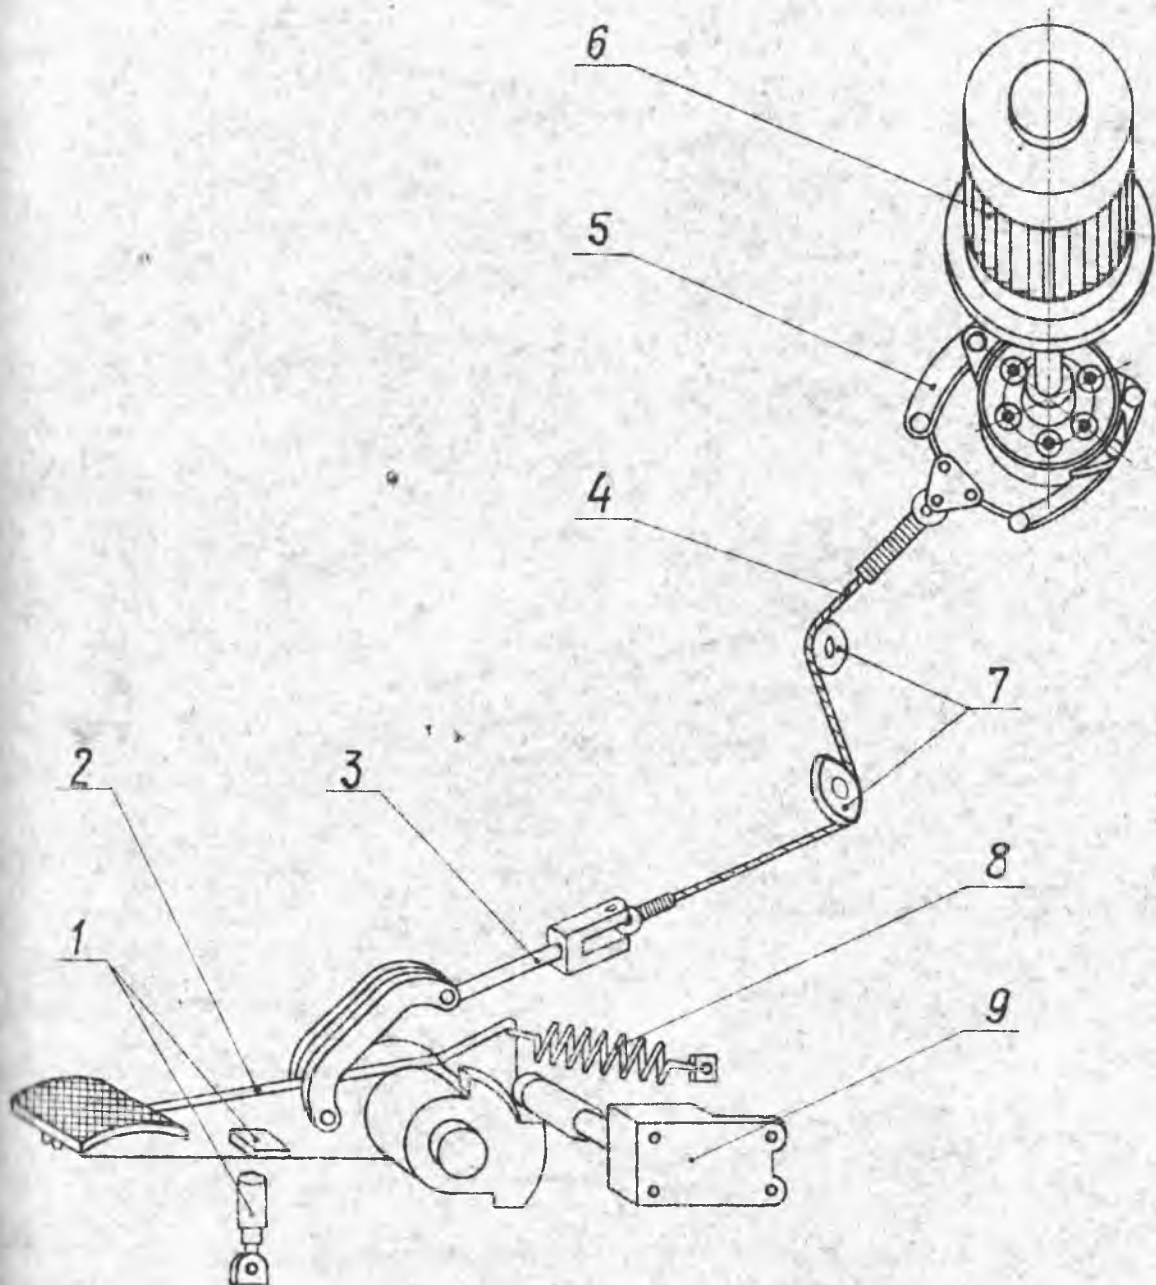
Кинематическая схема механизма управления тормозом поворота.
